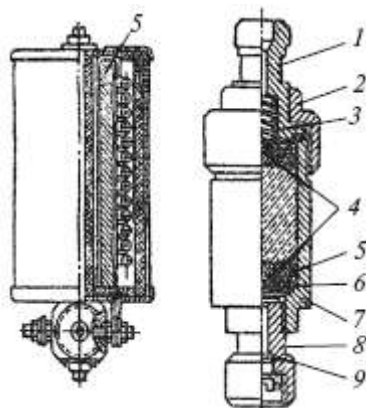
Осушитель углекислого газа: 1 – втулка; 2 – накидная гайка; 3 – пружина; 4 – сетки; 5 – фильтр; 6 – сетчатая шайба; 7 – корпус; 8 – штуцер; 9 – сетка
